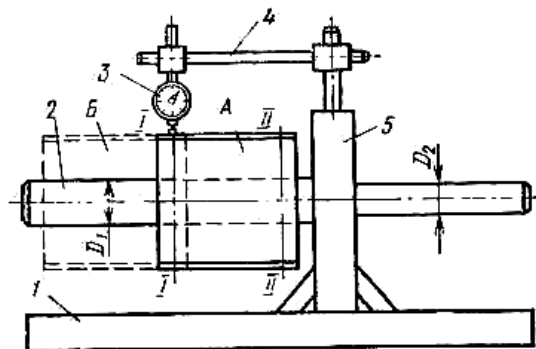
Контрольно-установочное приспособление для сборки фрез небольшого размера: *1* — основание, *2* — оправка, *3* — индикатор, *4* — штатив, *5* — стойка
